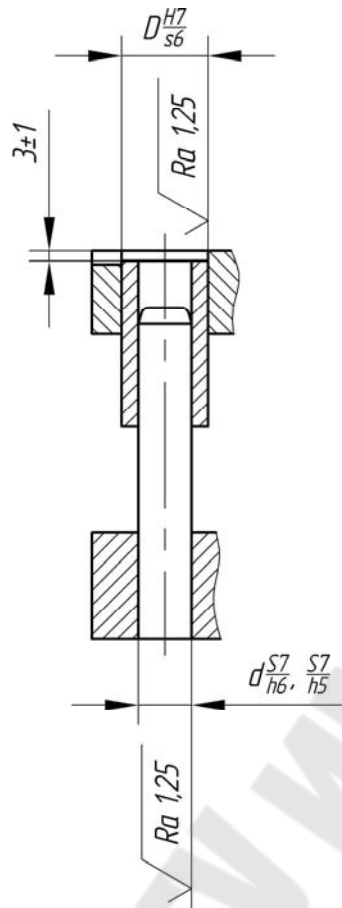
Способ закрепления деталей направляющих узлов скольжения
